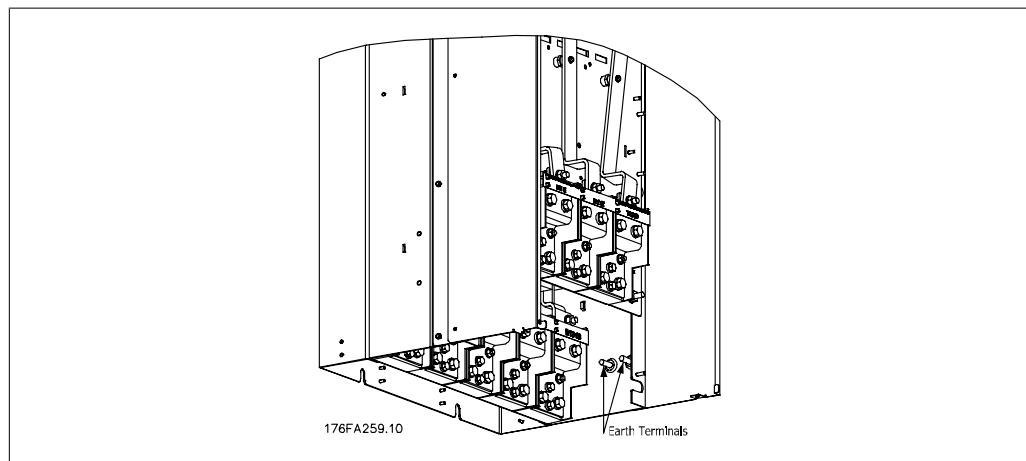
Jordklemmernes positioner IP00, E-kapslinger
